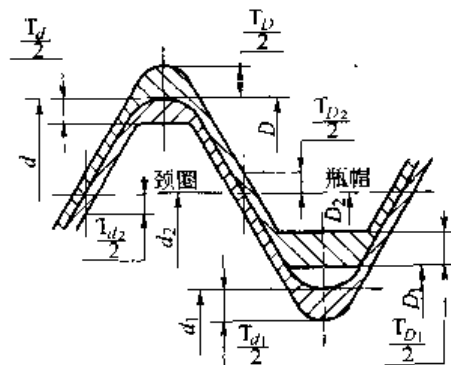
气瓶圆柱管螺纹的公差带
